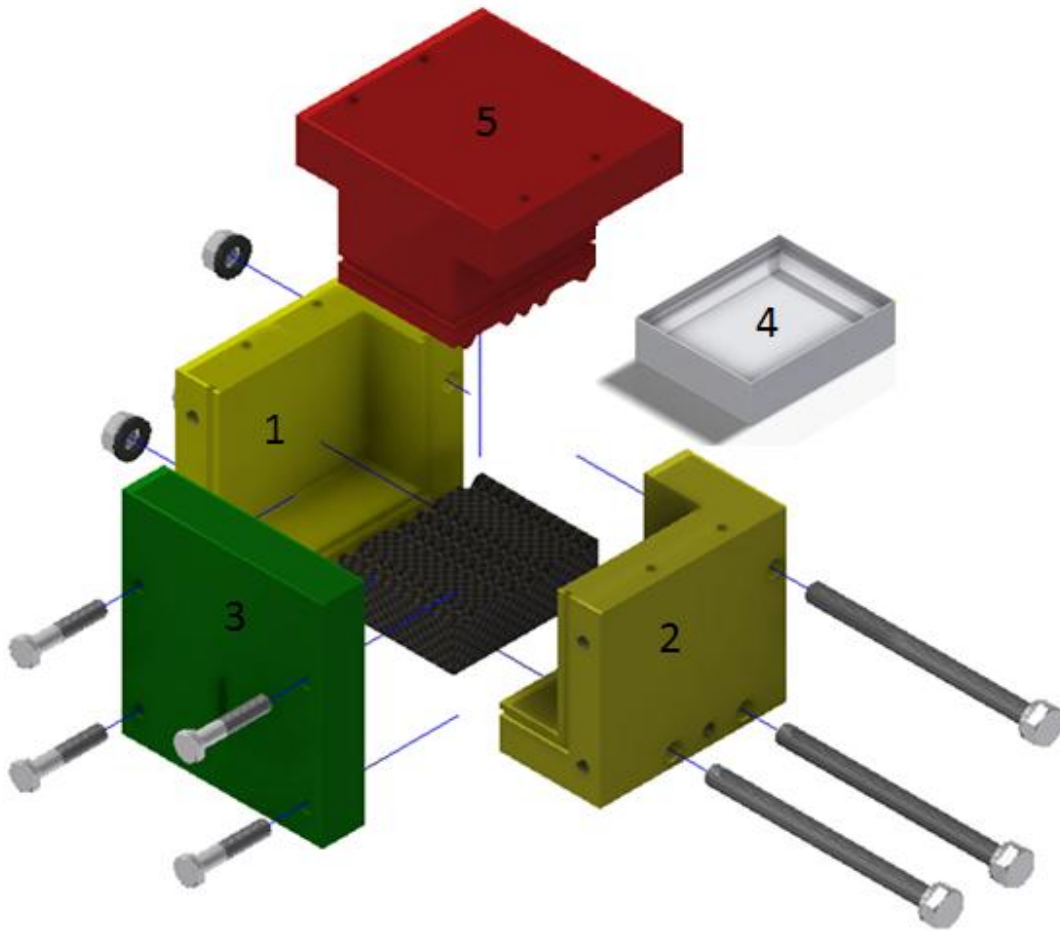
MOLDE PARA FABRICACION DE PRENSAS DE UN TRASPORTADOR DE HUESO CON RIEL EN FORMA DE "I". EXPLOSIONADO.
